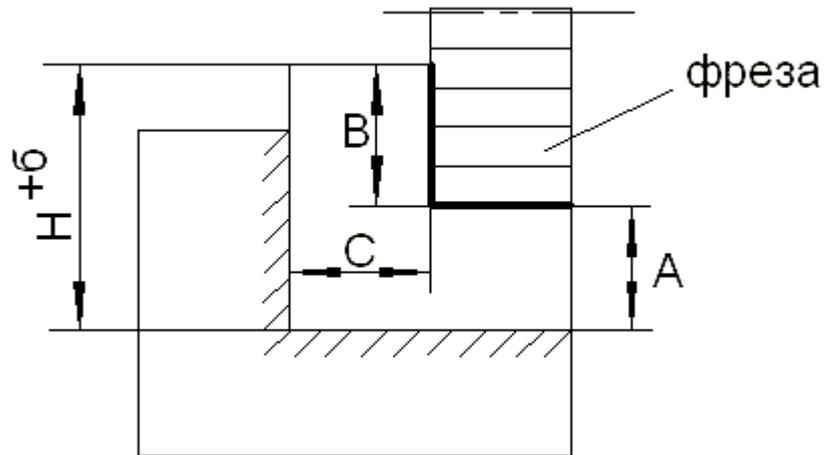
Схема базирования детали при фрезеровании уступа
